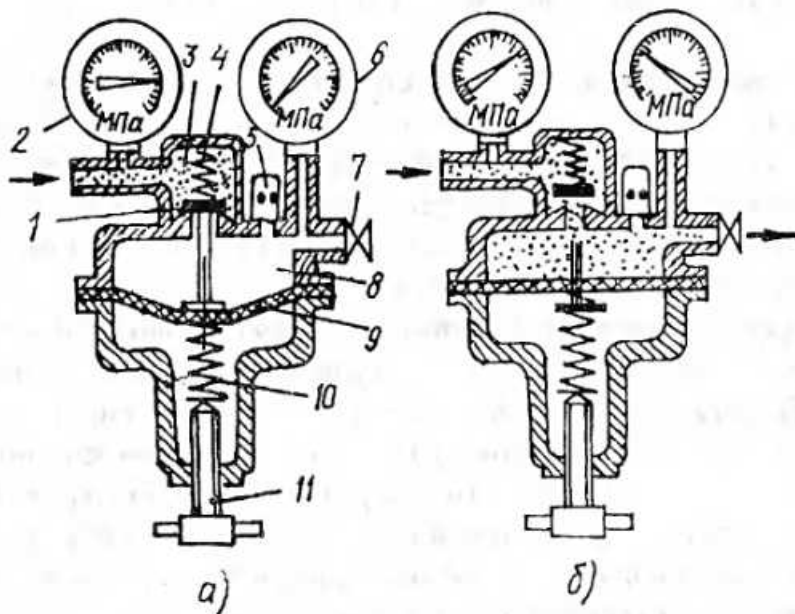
Схеми конструкції і роботи одноступінчатого редуктора:
